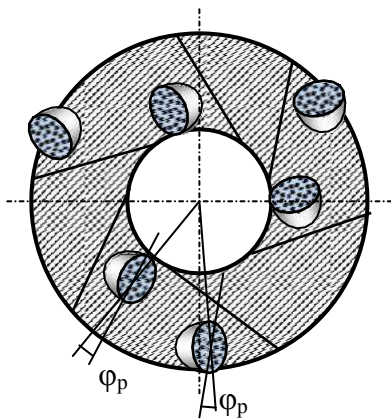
Схема установки резцов с *PDC* на торце инструмента для обеспечения отрицательного угла резания со скважинно- и кernoобразующими боковыми поверхностями
